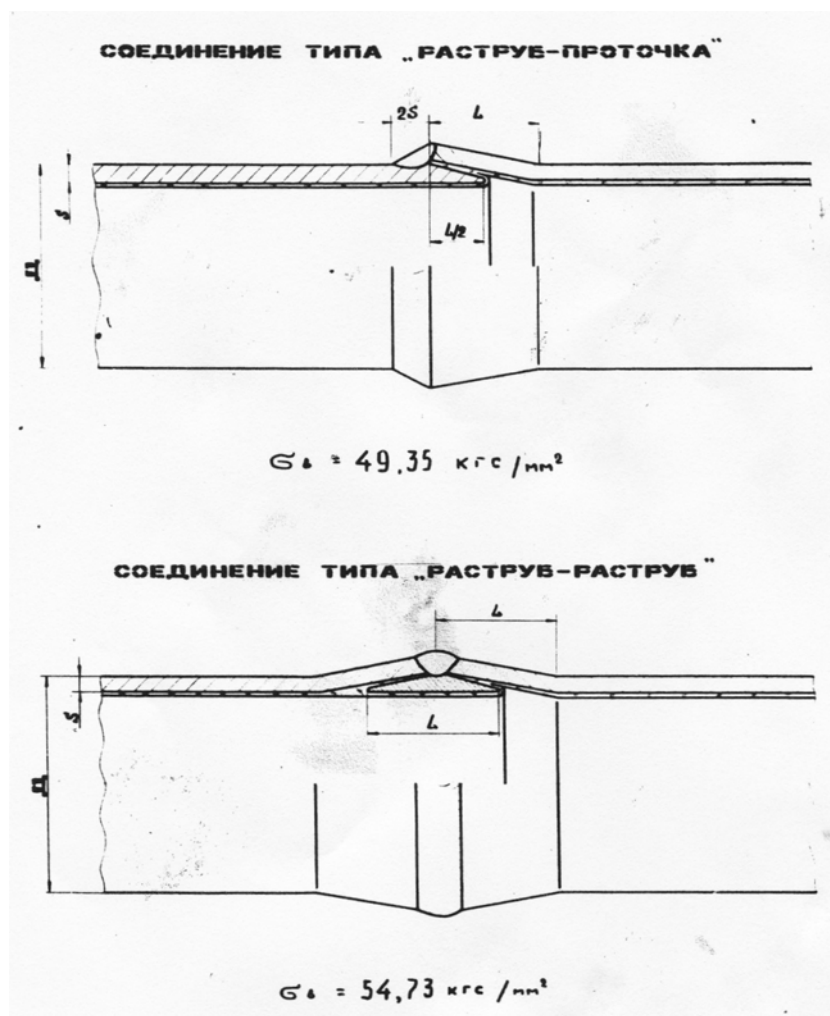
Сварные соединения труб со специальной предварительной формовкой их торцов, обеспечивающего защиту места стыка стеклянным покрытием.
